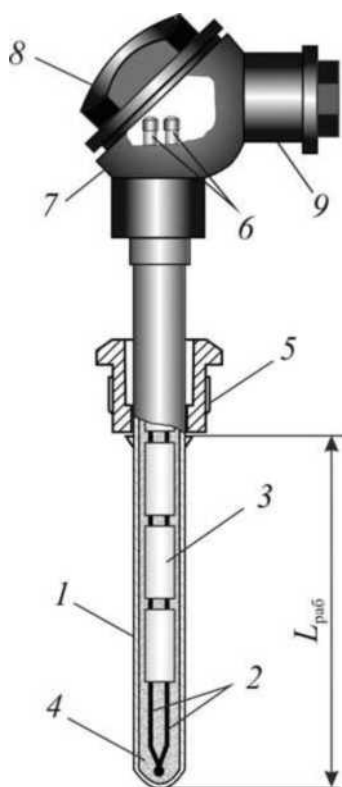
Конструкція термопари: 1 - захисний чохол; 2 - термоелектроди; 3 - ізоляційні намиста; 4 - порошок; 5 - штуцер; 6 - розетка з клемми; 7 - головка; 8 - кришка; 9 - штуцер під кабель
